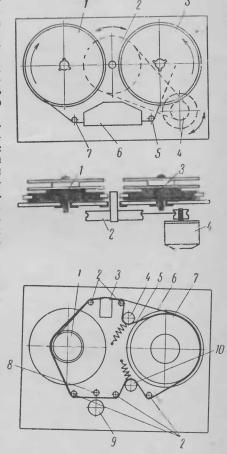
Кинематическая схема ленто-протяжного механизма.
